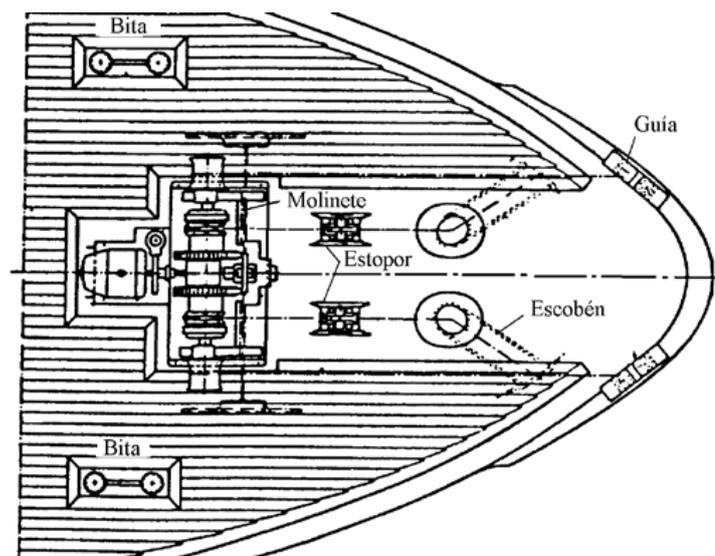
Vista en planta de la disposición del molinete sobre cubierta de proa. Fuente: Esteve-Pérez, J.A (s.f.). *Construcción Naval
